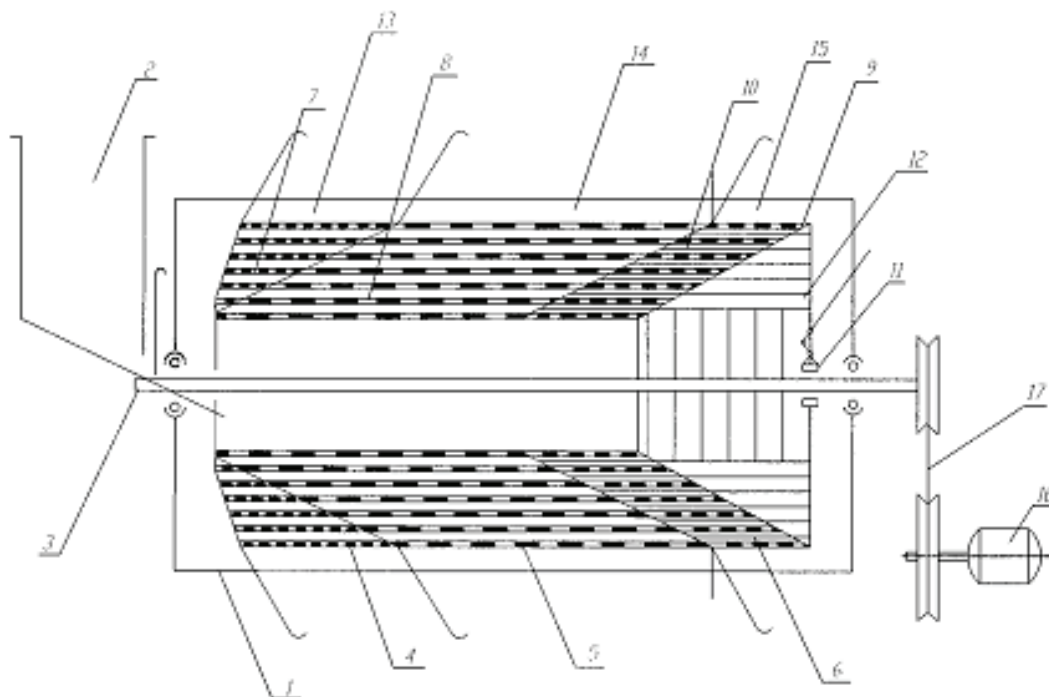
Схема зерноочистительной машины: 1 — цилиндрический корпус; 2 — питающее устройство; 3 — приводной вал; 4 — левый блок; 5 — средний блок; 6 — правый блок; 7 — размер отверстий левого блока; 8 — размер отверстий среднего блока; 9 — размер отверстий правого блока; 10 — прижимные полотна; 11 — устройство для перемещения прижимных полотен; 12 — щелевидные отверстия; 13 — приемник мелкой фракции; 14 — приемник основной фракции; 15 — приемник длинной фракции; 16 — электродвигатель; 17 — клиноременная передача
